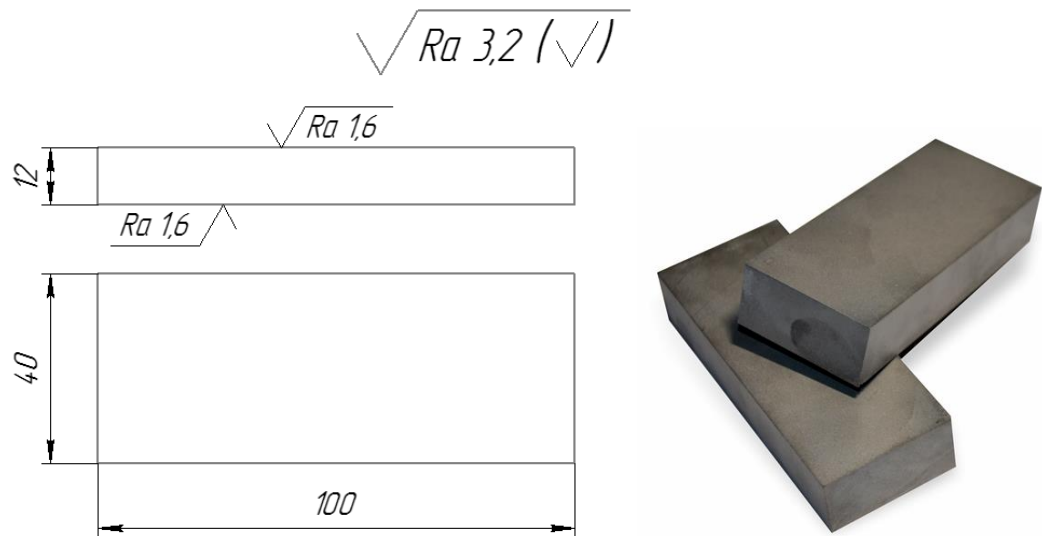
Заготовки из твердосплавной пластины ВК8 ГОСТ 19106-73 для шлифования периферией круга
